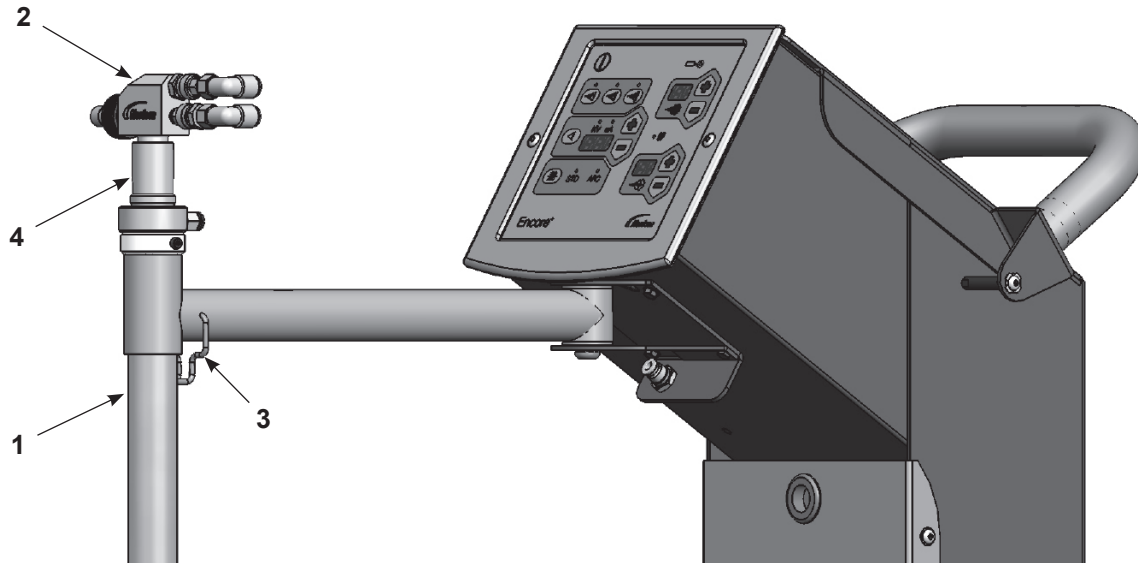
Installation du tube de prélèvement pour pistolet Encore LT et de la pompe
